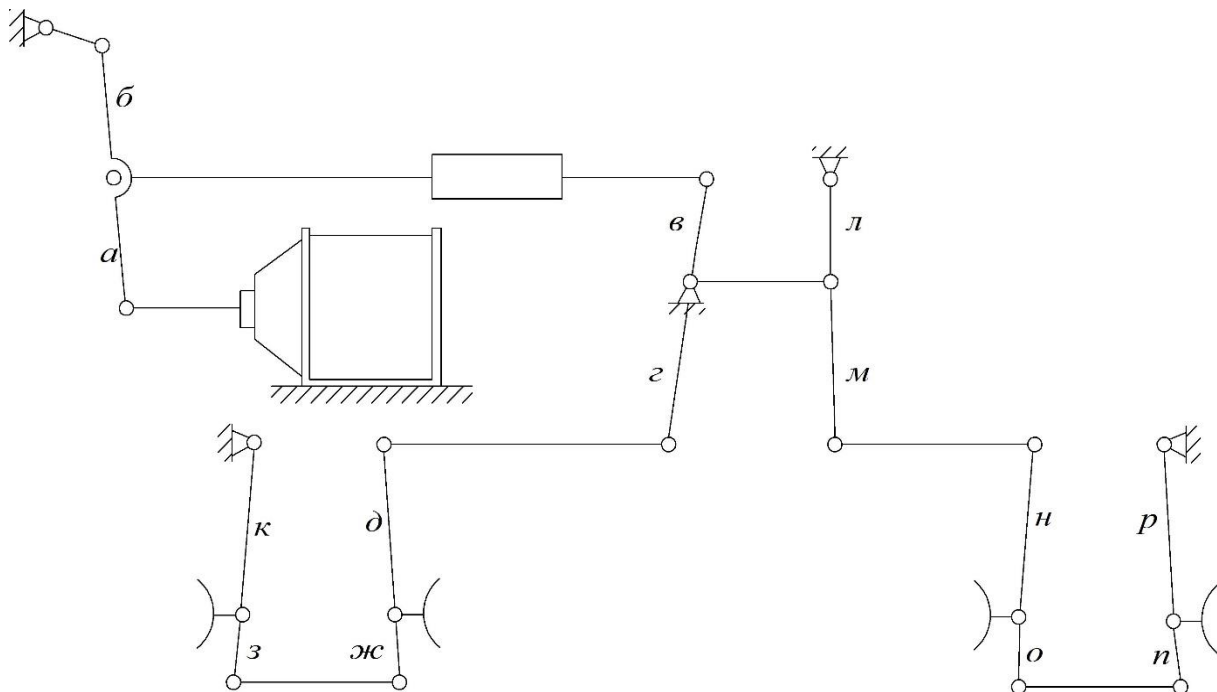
Розрахункова схема ГВП вагона для перевезення зерна
